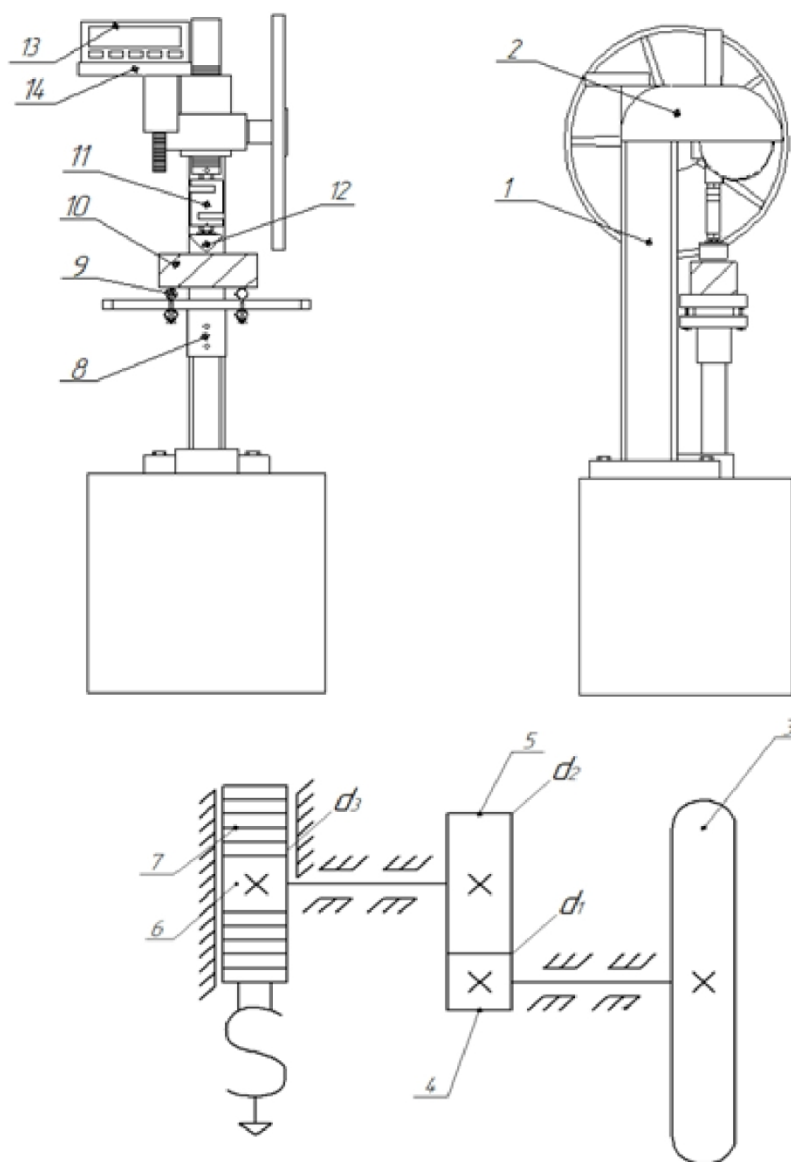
Устройство и кинематическая схема стэнда для создания разрушающей нагрузки и контроля изгибной прочности формованной торфяной продукции
